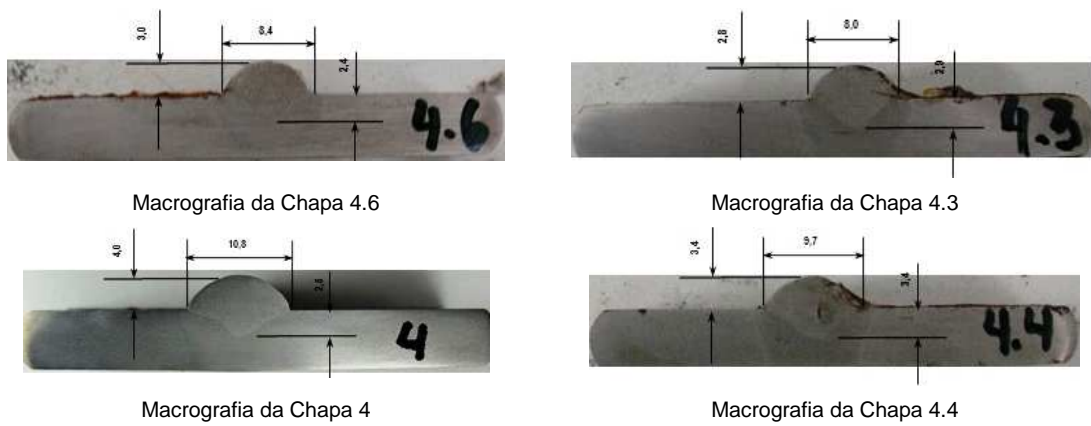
Macrografias com altura do reforço (r), largura do cordão de solda (b) e a penetração das soldas com $Ar+10\%CO_2+2\%H_2$.
